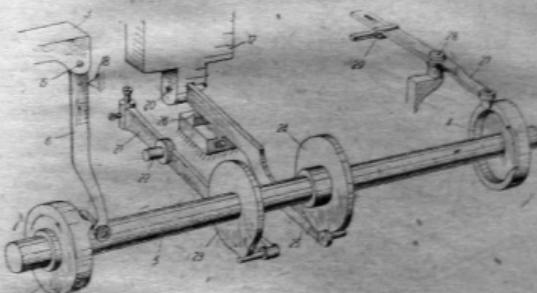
Полуавтомат Сафаг для изготовления фасонных фрез.
